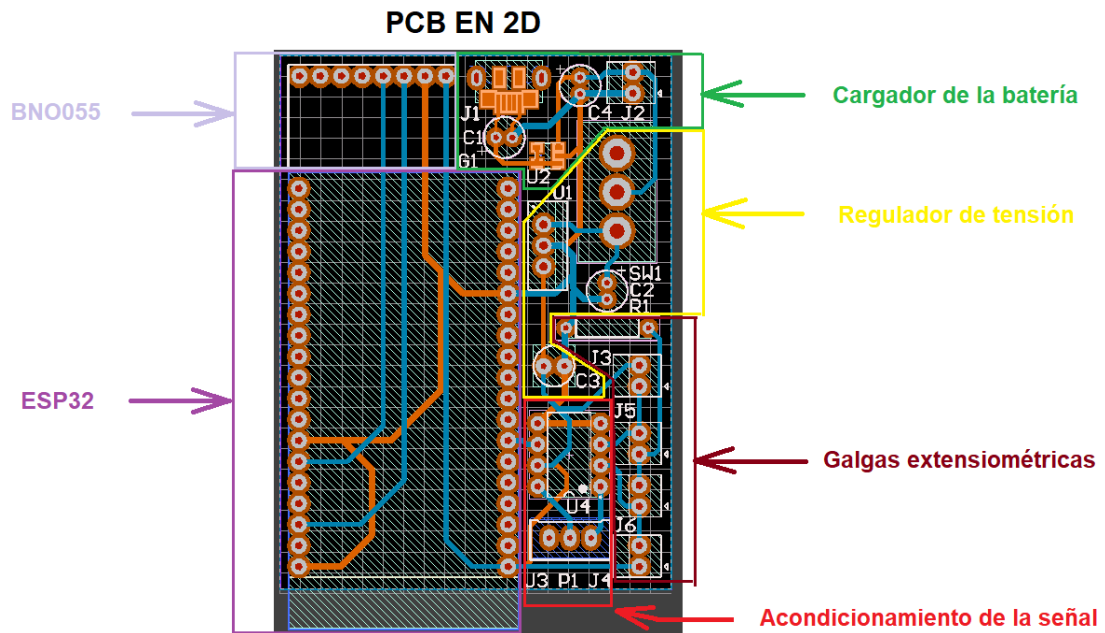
Diseño PCB en 2D del detector de la cojera de una pata
